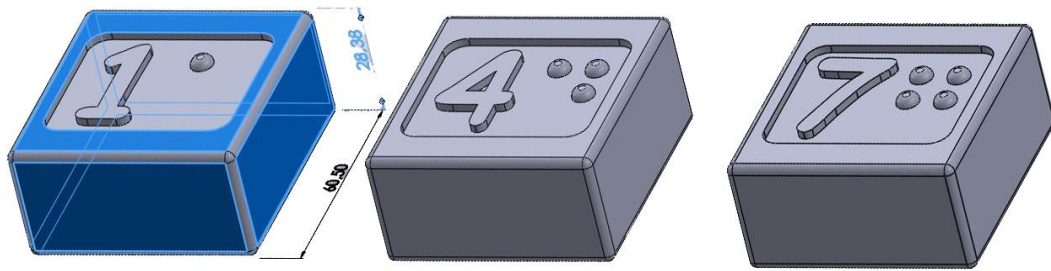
Piezas planas con base cuadrada con dimensiones generales
